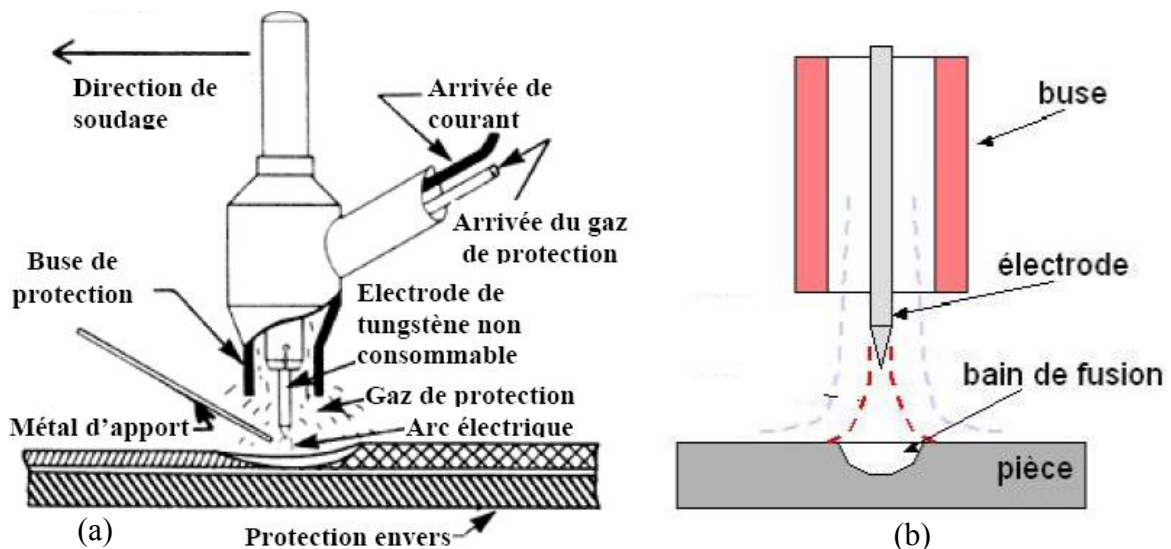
Représentation schématique du principe du soudage TIG [121]
